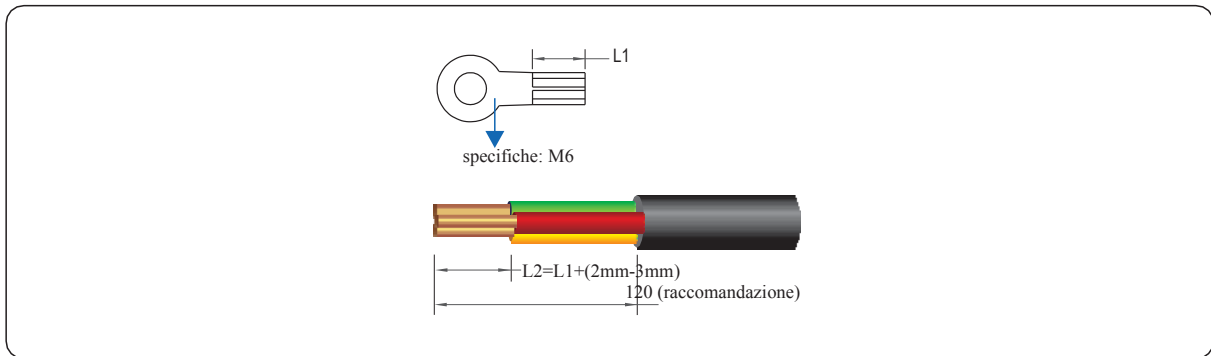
Lunghezza cavo spelato (unità: mm)
